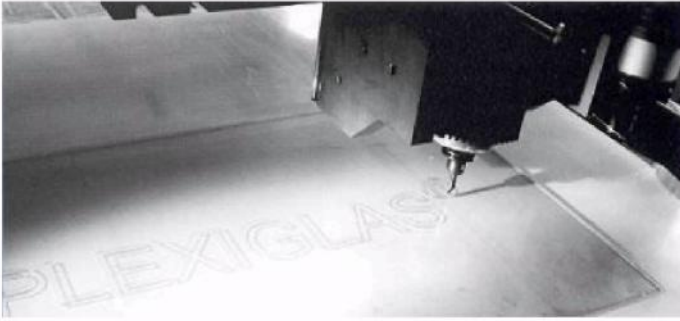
Гравирование при помощи машины с ЧПУ портального типа; одно- кромочная фреза
